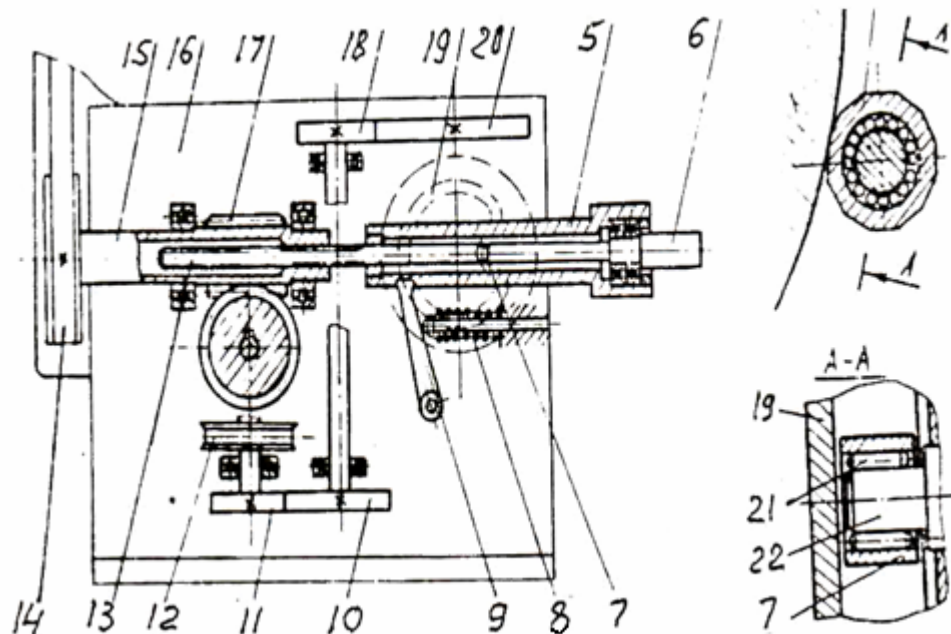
Схема кулачкового механізму з нерівномірним рухом привода подачі
